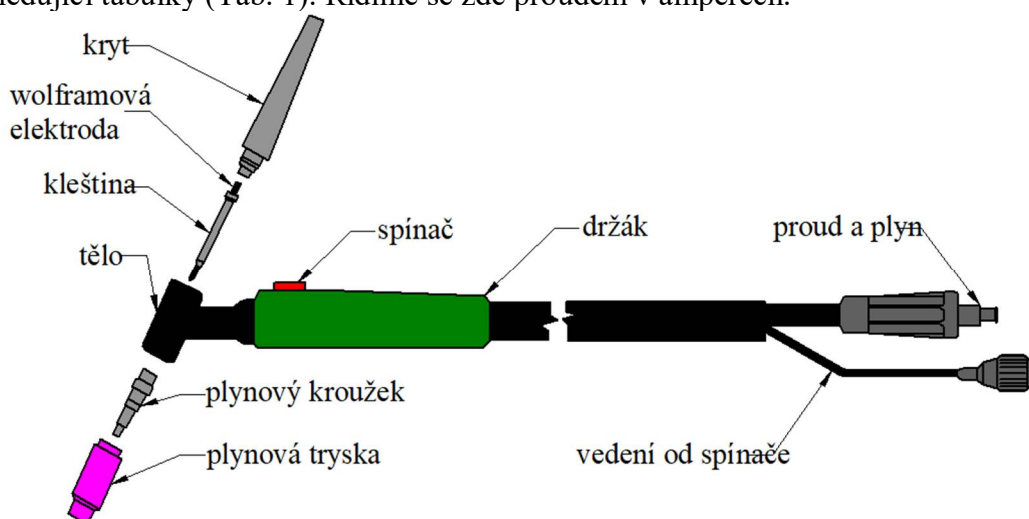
Základní sestava zařízení pro svařování WIG Stejnosměrným proudem [15]
